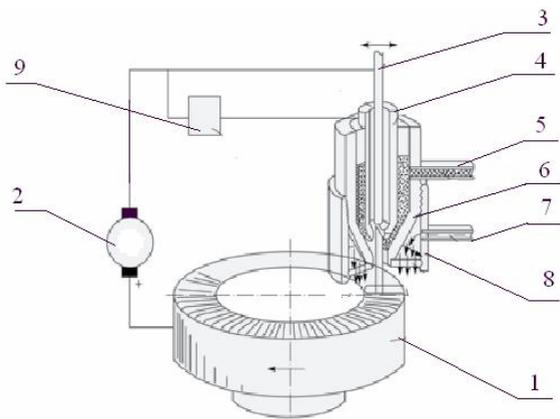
Схема плазменно-порошковой наплавки: 1 – изделие; 2 – источник питания плазменной дуги; 3 – вольфрамовый электрод; 4 – стабилизирующее сопло плазмотрона; 5 – ввод транспортирующего газа с порошком; 6 – фокусирующее сопло; 7 – ввод защитного газа; 8 – защитное сопло; 9 – устройство поджига дуги
